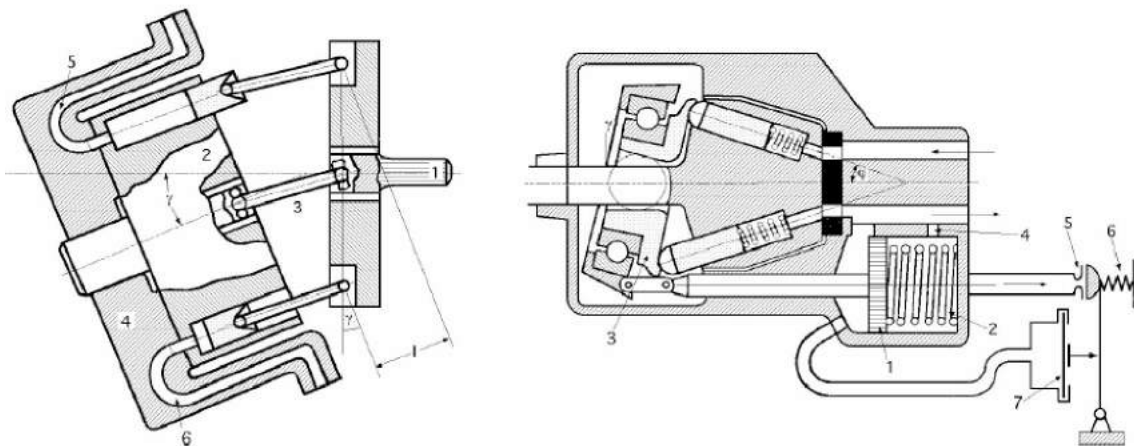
Compresores de pistones, con bloque de pistones inclinado y regulable.
